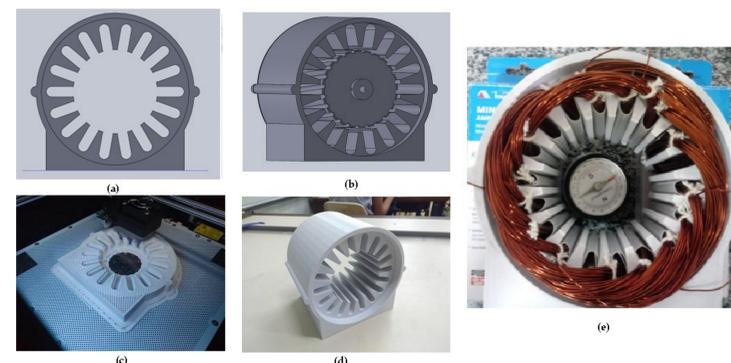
(a) Corte frontal do MIT - (b) Visão lateral do estator e rotor do MIT - (c) Processo de impressão do rotor - (d) Estator impresso - (e) Teste do campo girante
